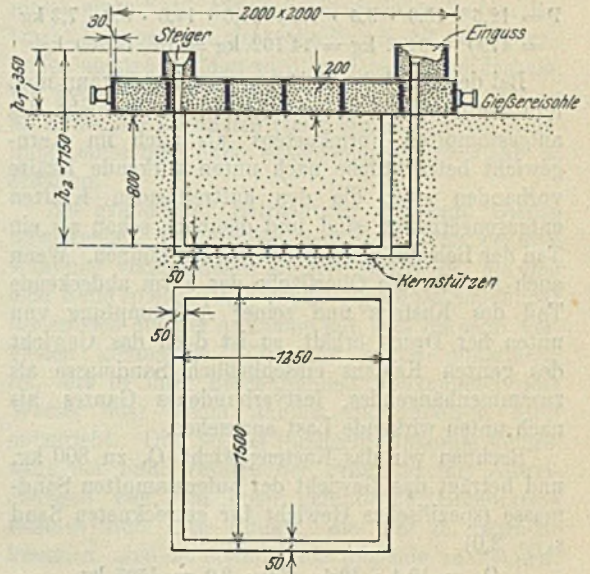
Form eines viereckigen Gefäßes mit Kern auf Stützen.
